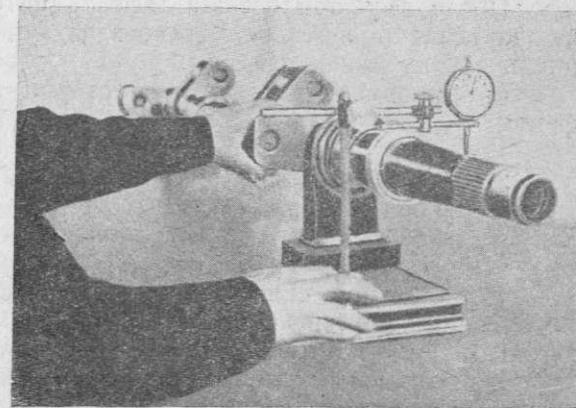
Проверка биения носка коленчатого вала индикатором.
